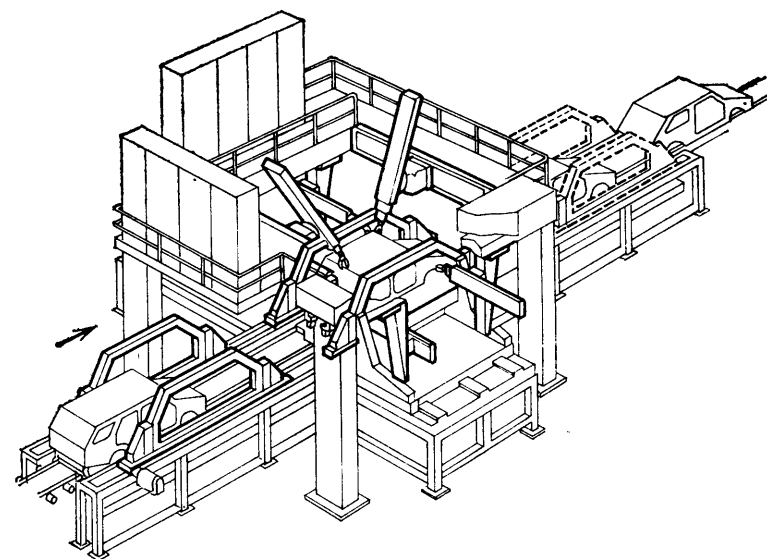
Ячейка формообразования и предварительной сварки кузовов пяти различных моделей
